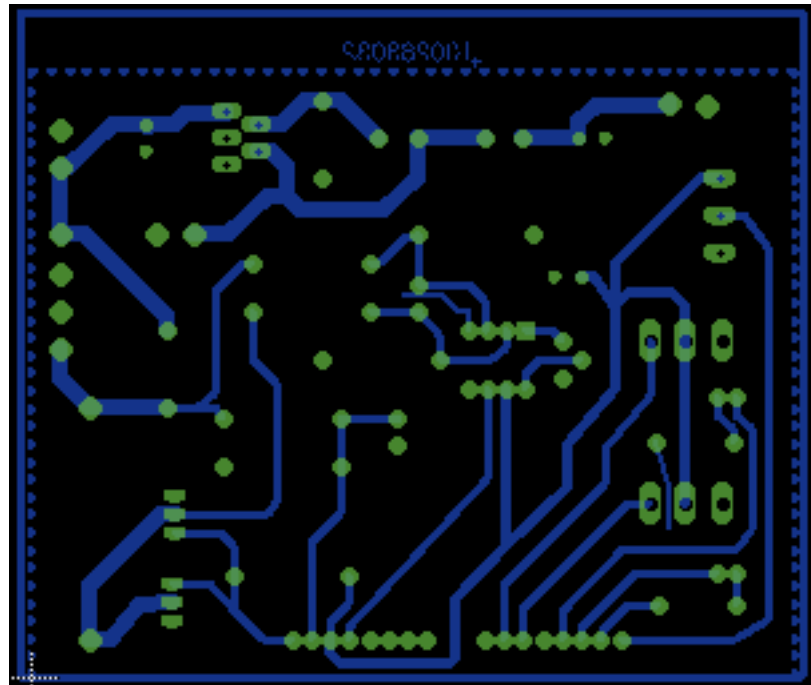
Rutas y PADs del circuito impreso PCB parte 1
